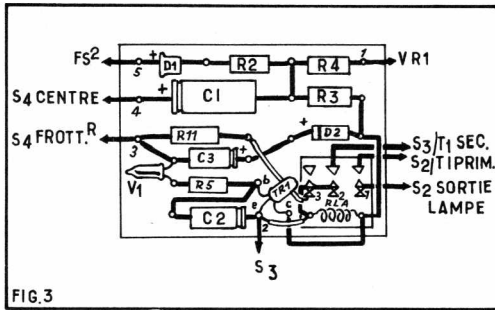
Disposition des composants sur la plaquette d'isolant.
